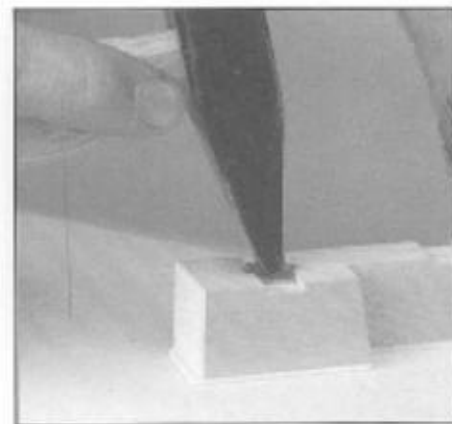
mit einem Hammer durch leichtes, vorsichtiges Klopfen geringfügig verringert.
